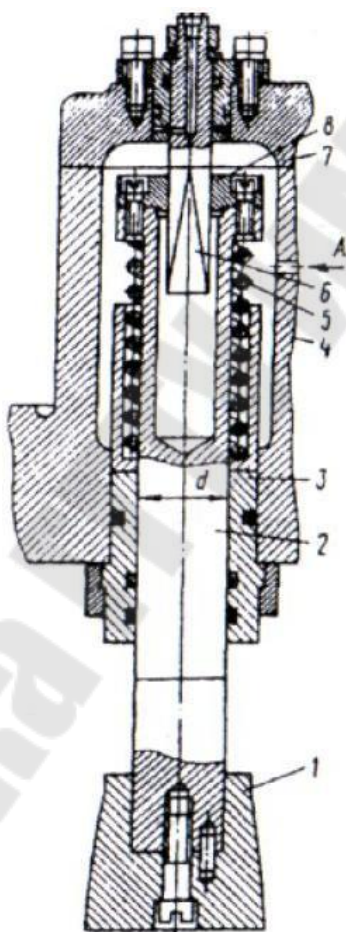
Конструкция узла плунжера активной прессовой головки
